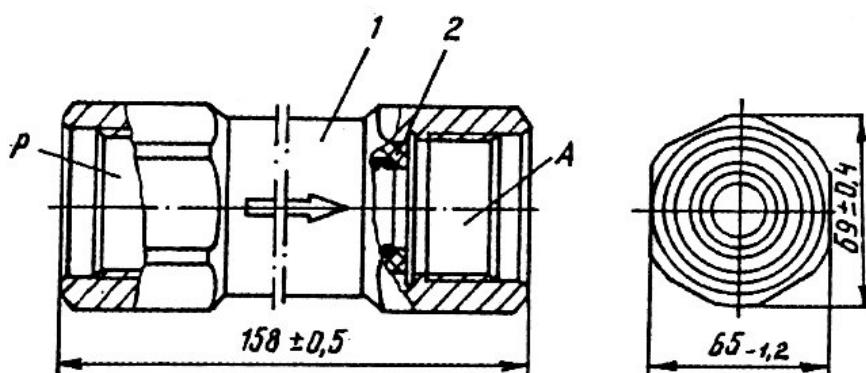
Общий вид обратного клапана типа 531.20.00
